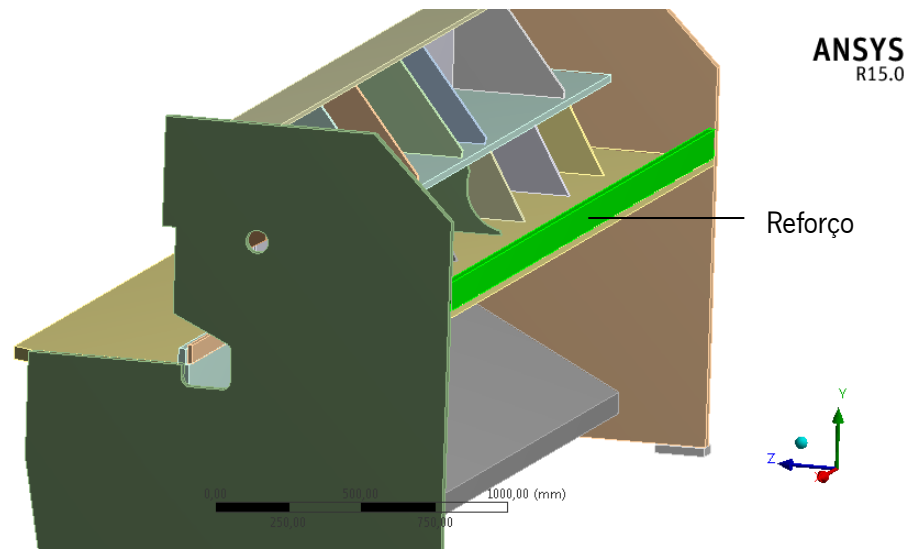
Detalhe do pormenor do perfil de secção retangular.
